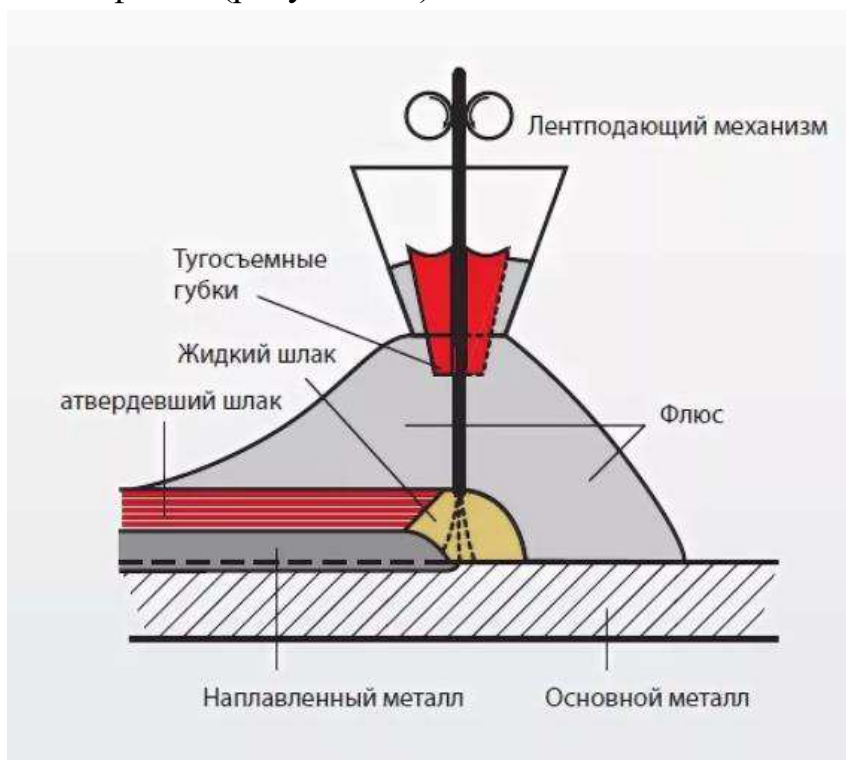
Схема дуговой наплавки под флюсом
